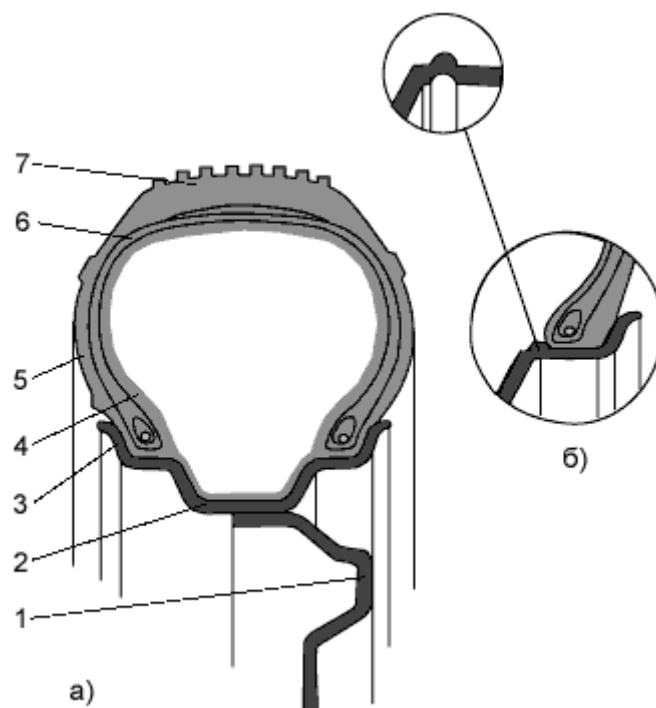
Колесо легкового автомобиля а) устройство колеса б) уплотняющий буртик на ободе бескамерной шины 1 - диск колеса; 2 - обод; 3 - борт; 4 - камера; 5 - боковина; 6 - корд; 7 - протектор
